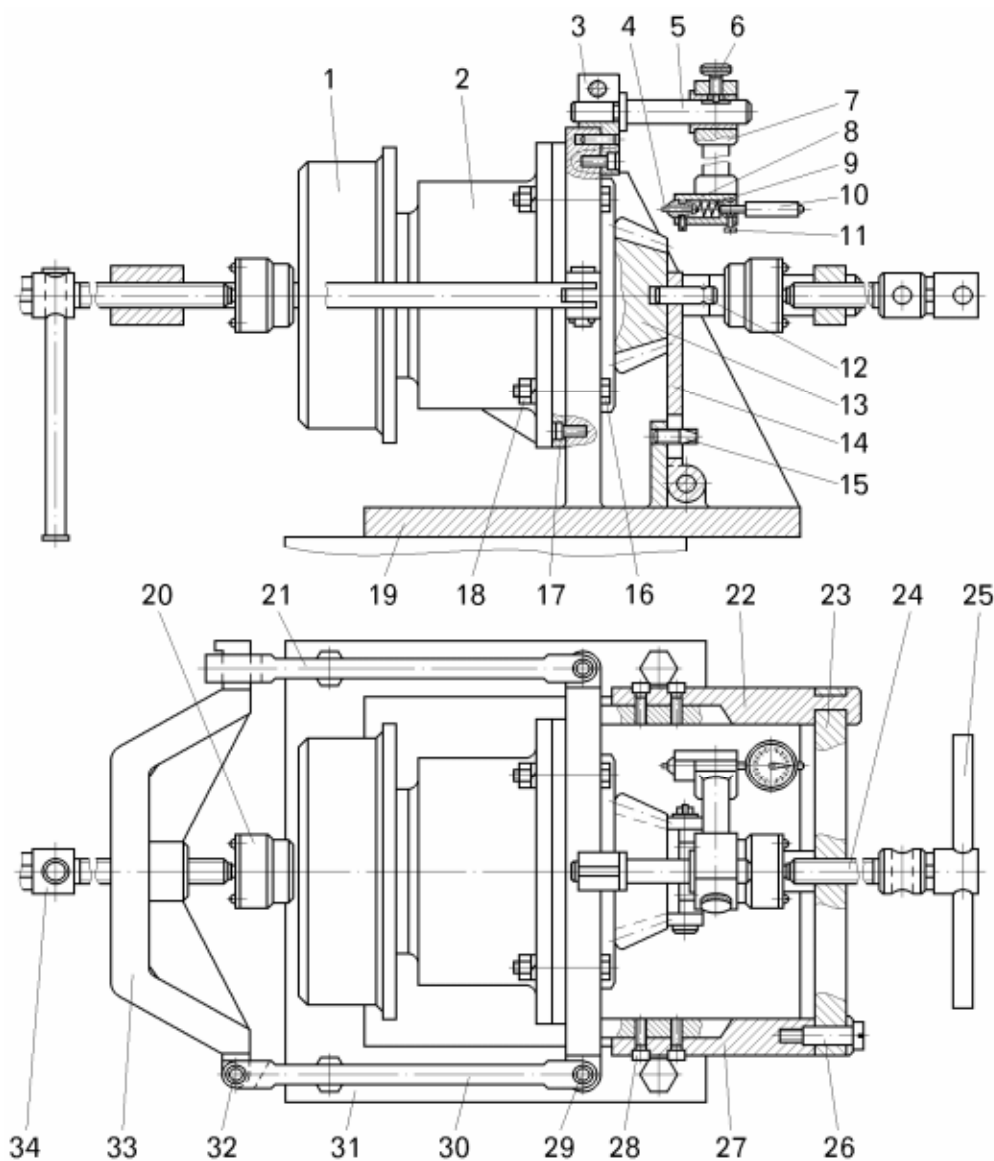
Стенд для разборки, сборки и регулировки зазора ведущей шестерни:
